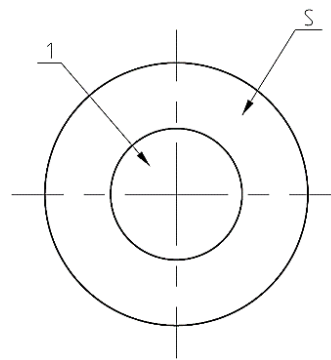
Вид на торец заготовки детали, имеющей отверстие
